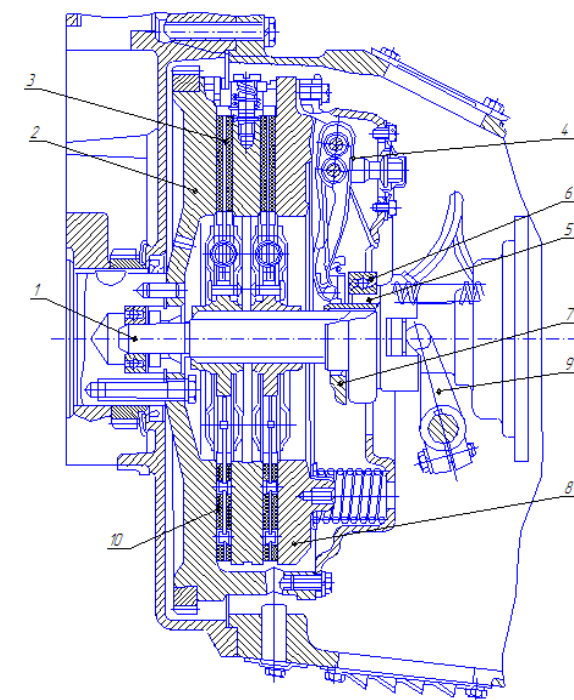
Общий вид существующего привода сцепления автомобиля КамАЗ: 1 - вал сцепления; 2 - маховик; 3 - ведомый диск; 4 - отжимной рычаг; 5 - муфта выключения сцепления; 6 - выжимной подшипник; 7 - упорное кольцо; 8 - задний нажимной диск; 9 - вилка выключения сцепления; 10 - передний ведомый диск.
